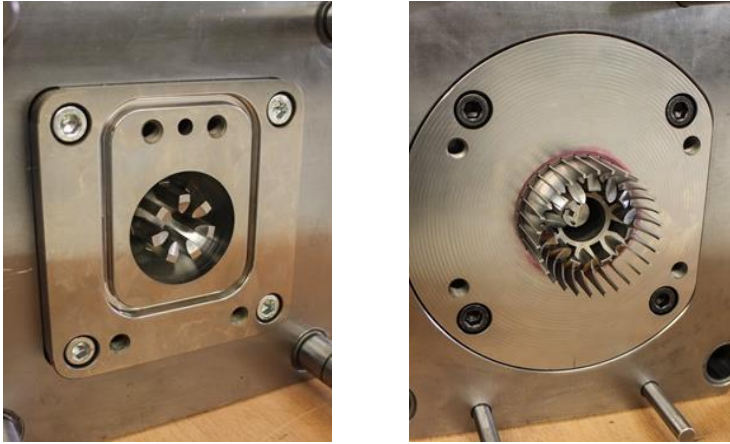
Düsenseite (links) und Auswerferseite (rechts) des Spritzgießwerkzeugs mit Formeinsatz für den kugelförmigen Leuchten-Kühlkörper
